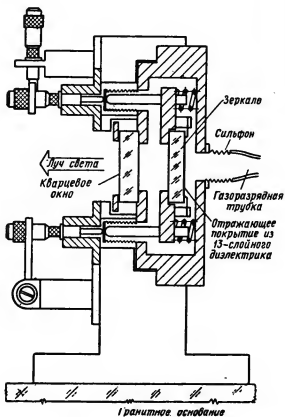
Устройство юстировочного приспособления головки газового генератора.
